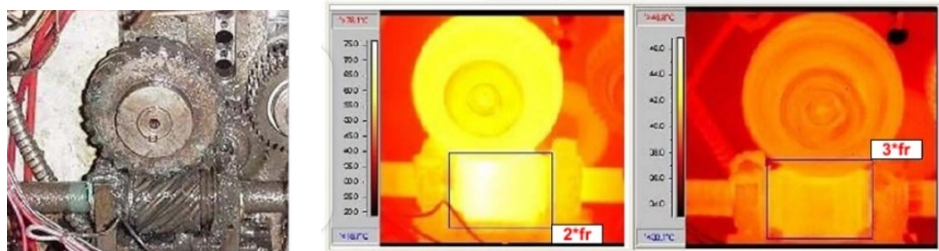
exemple de défaut d'engrenage, avant et après la corrosion
